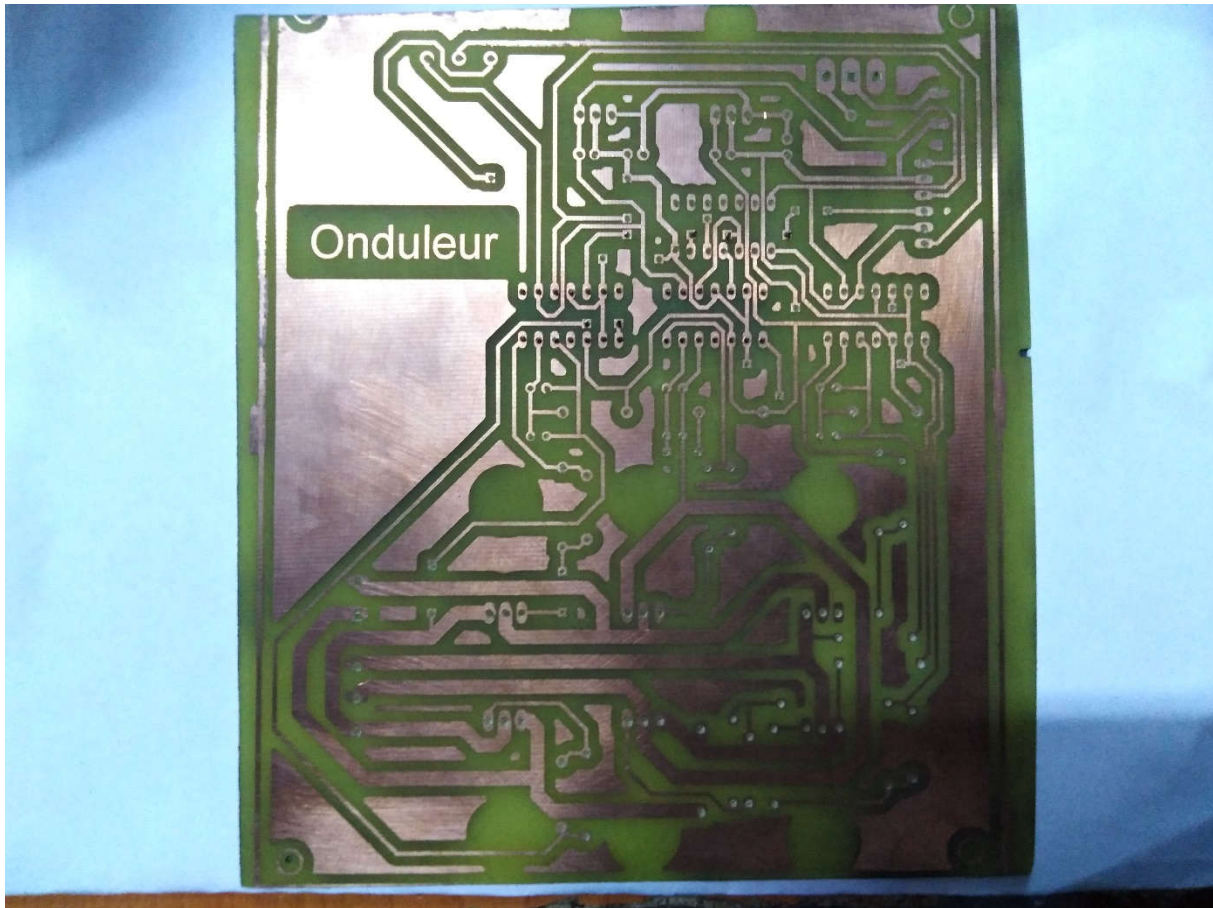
Circuit imprimé de l'onduleur (face de soudure)
